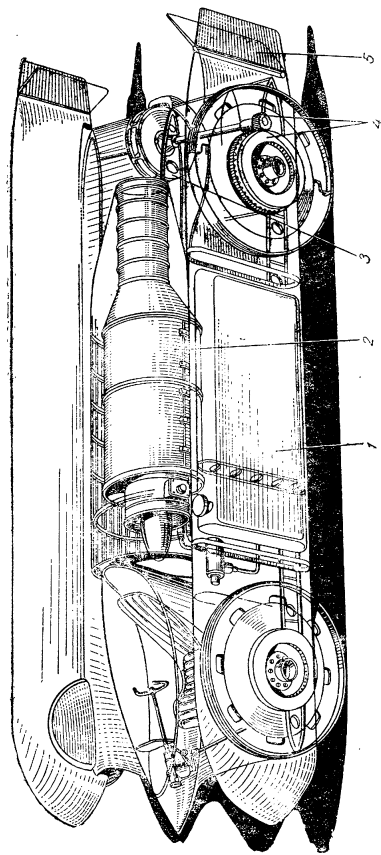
Рекордный автомобиль Л. Шмидта: 1 — топливный бак; 2 — газотурбинный двигатель; 3 — дополнительная газовая турбина для привода воздушных колес; 4 — редуктор; 5 — воздушный тормоз
